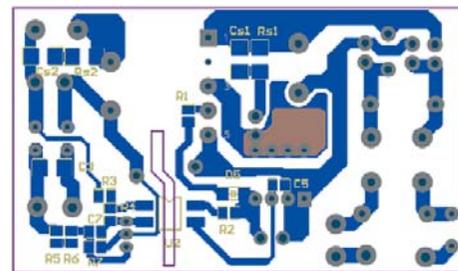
Рисунок печатной платы драйвера с расположением деталей на ней
